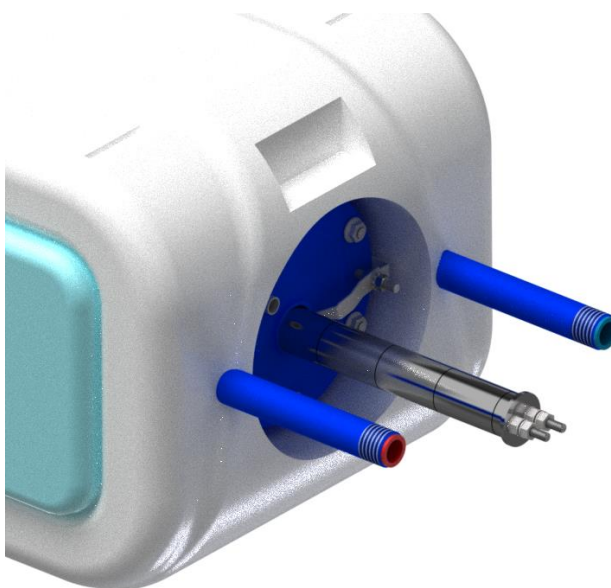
Vyražení použitého materiálu na komponentách pro snadné třídění.
